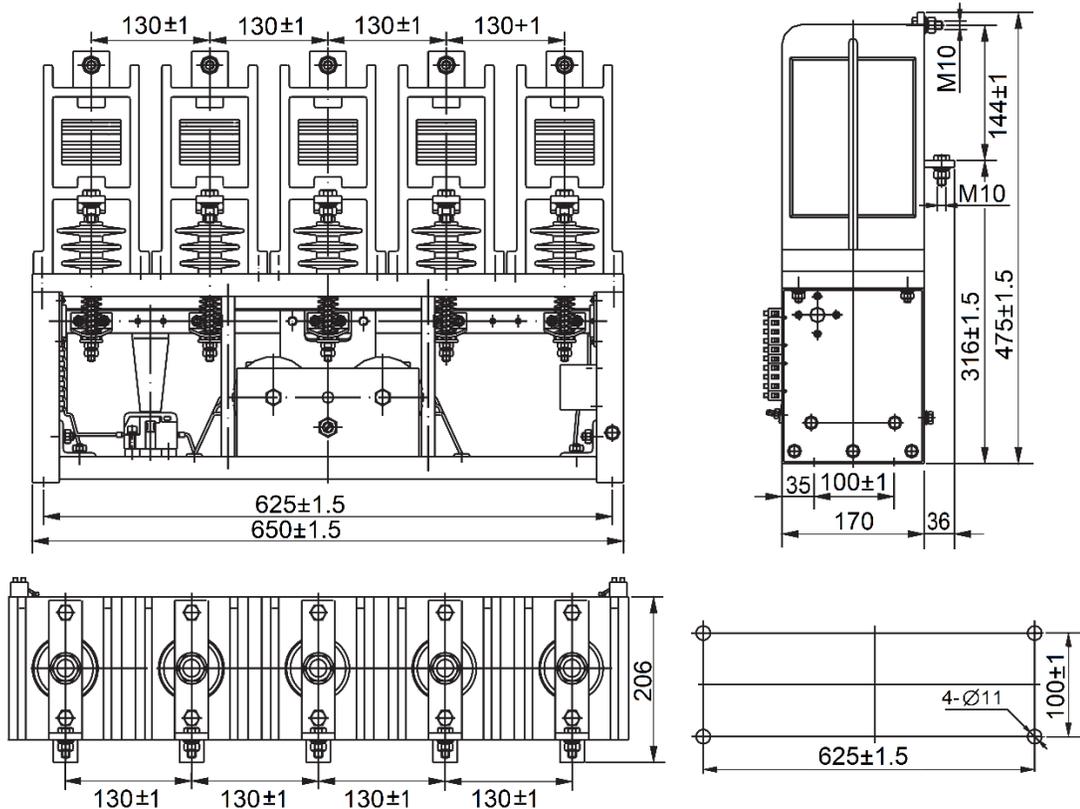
Габаритные размеры контакторов КВТ-6 на номинальные токи 160, 250, 400, 630 А пяти полюсного исполнения и размеры монтажной площадки.
